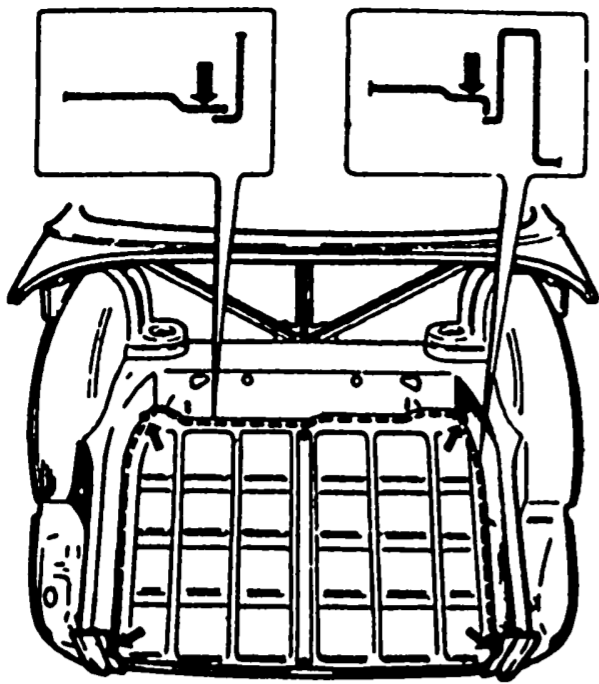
Замена панели задка. Пунктиром обозначены линии рубки, точками — швы контактной сварки. На основном виде стрелками показаны места газовой сварки, стрелками на фрагменте — места рубки
